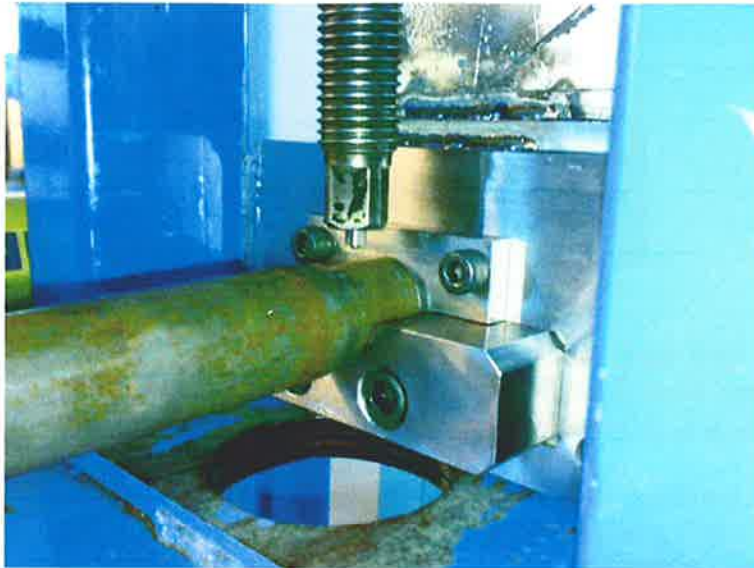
Montaje del sistema dimpling de la prueba.
